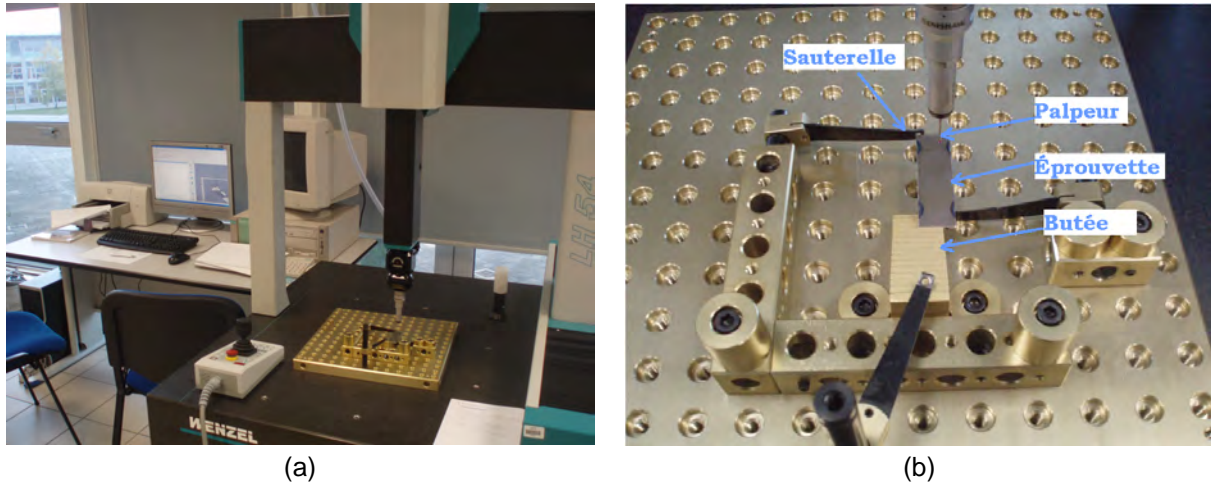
MMT, (a) vue d'ensemble, (b) montage d'une éprouvette serrée d'un côté par une butée et d'un autre côté par une sauterelle
